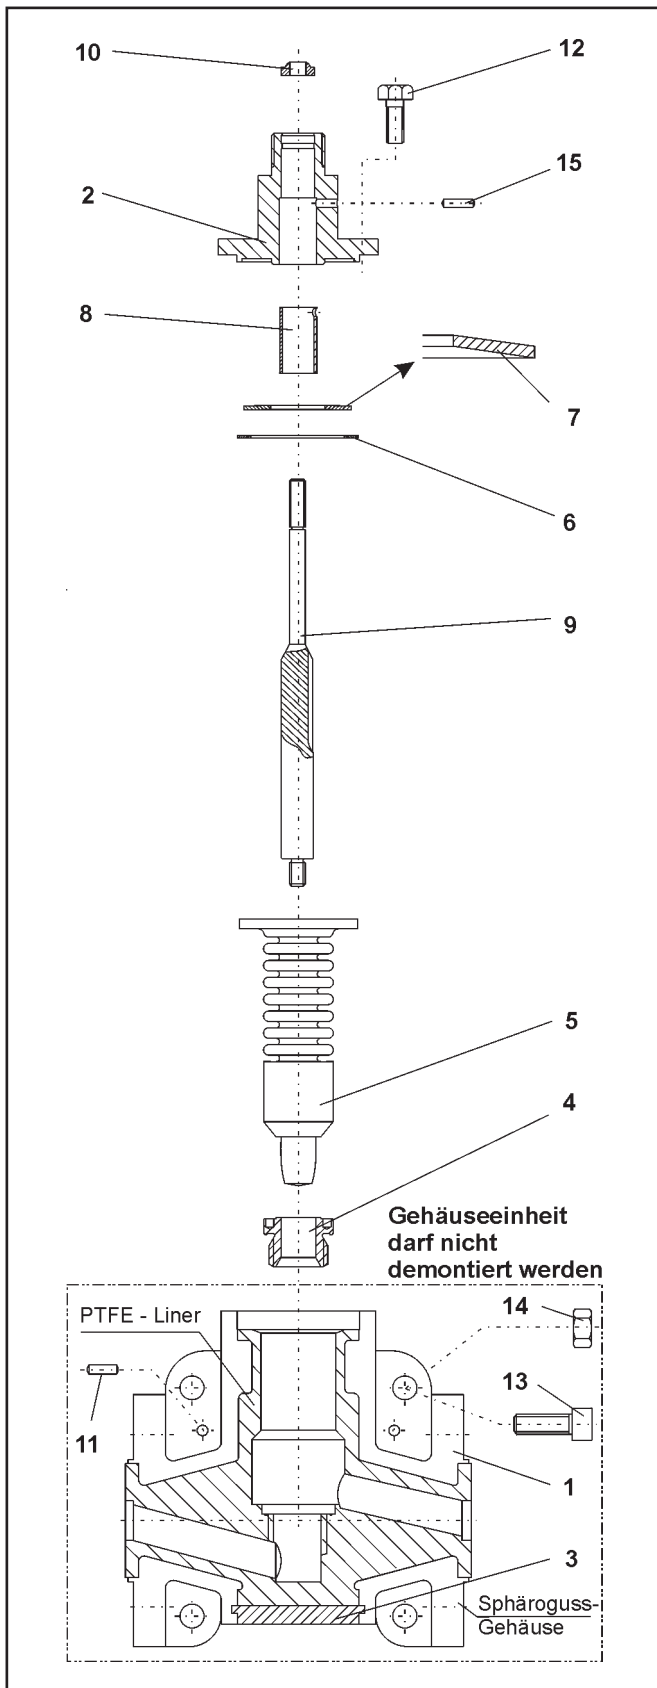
Explosionszeichnung des Mikroventils BR 6a
